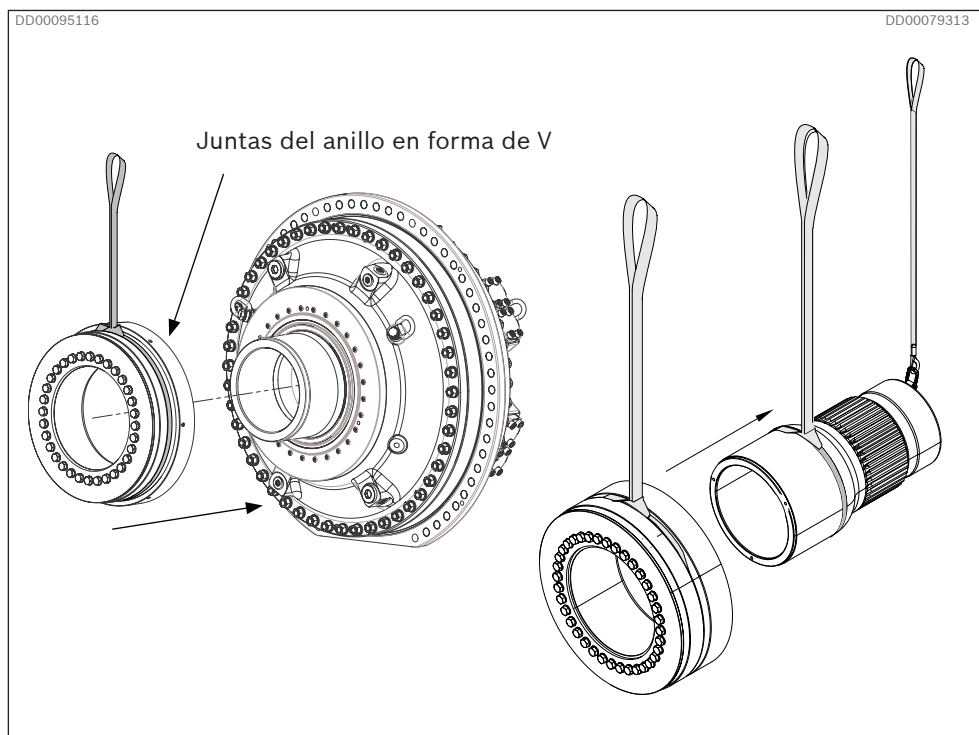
Instalación del disco compresor en el eje del adaptador o el motor de acoplamiento
